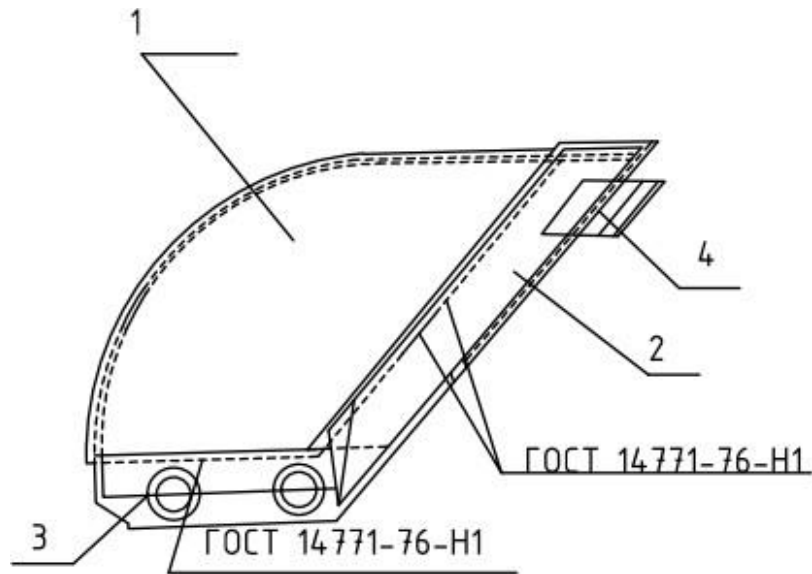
Складання і зварювання боковин і ножів.
